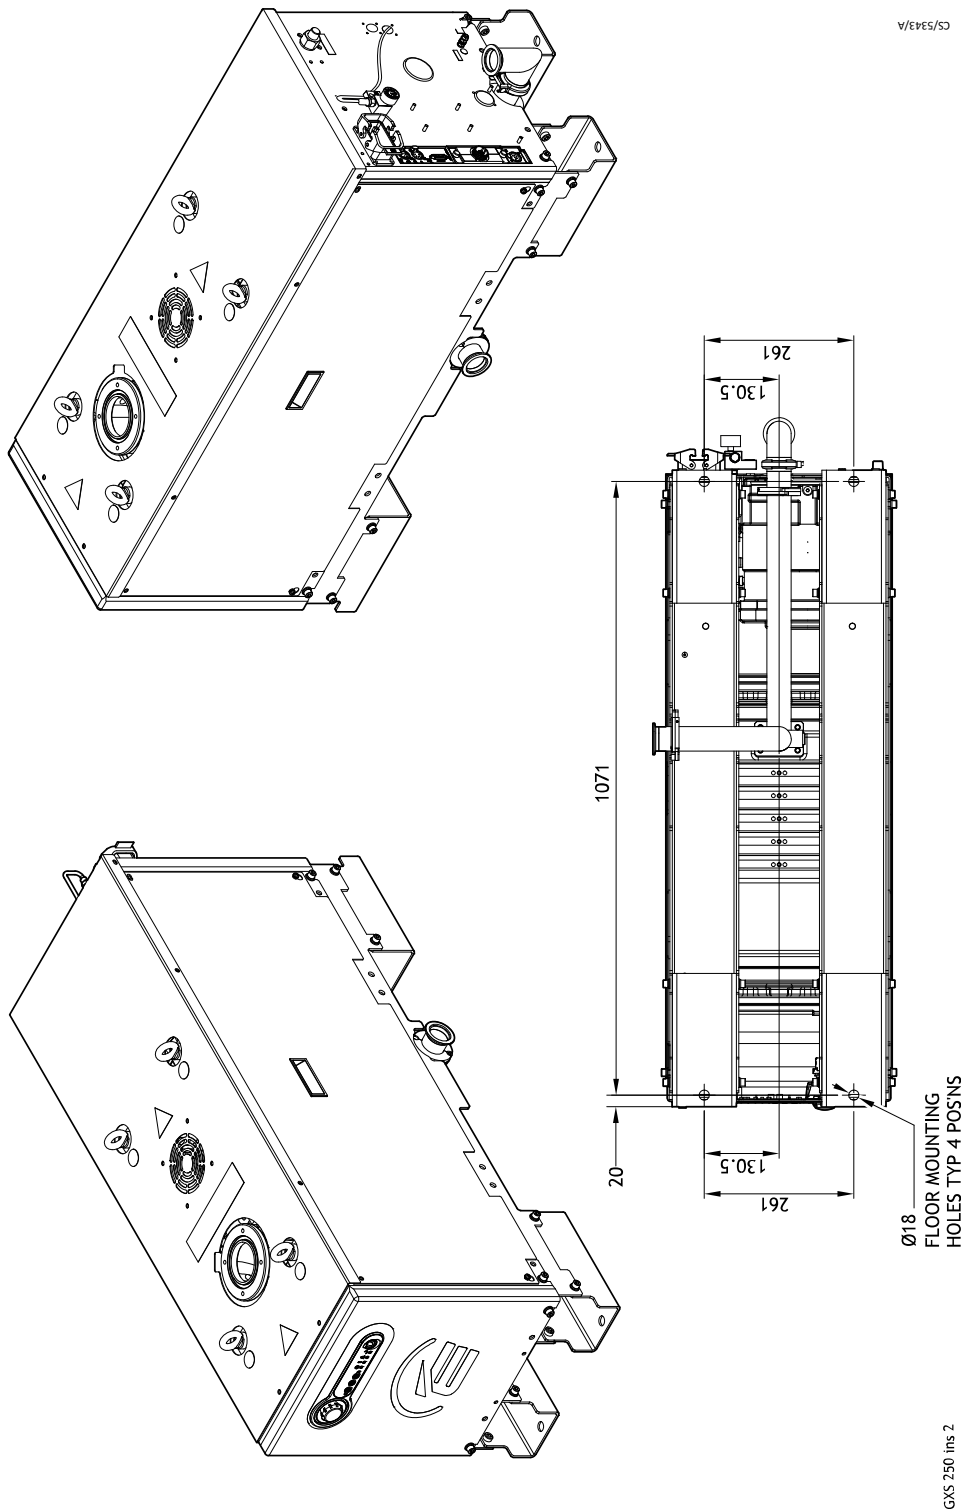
GX5250 Installationszeichnung (Blatt 3)
